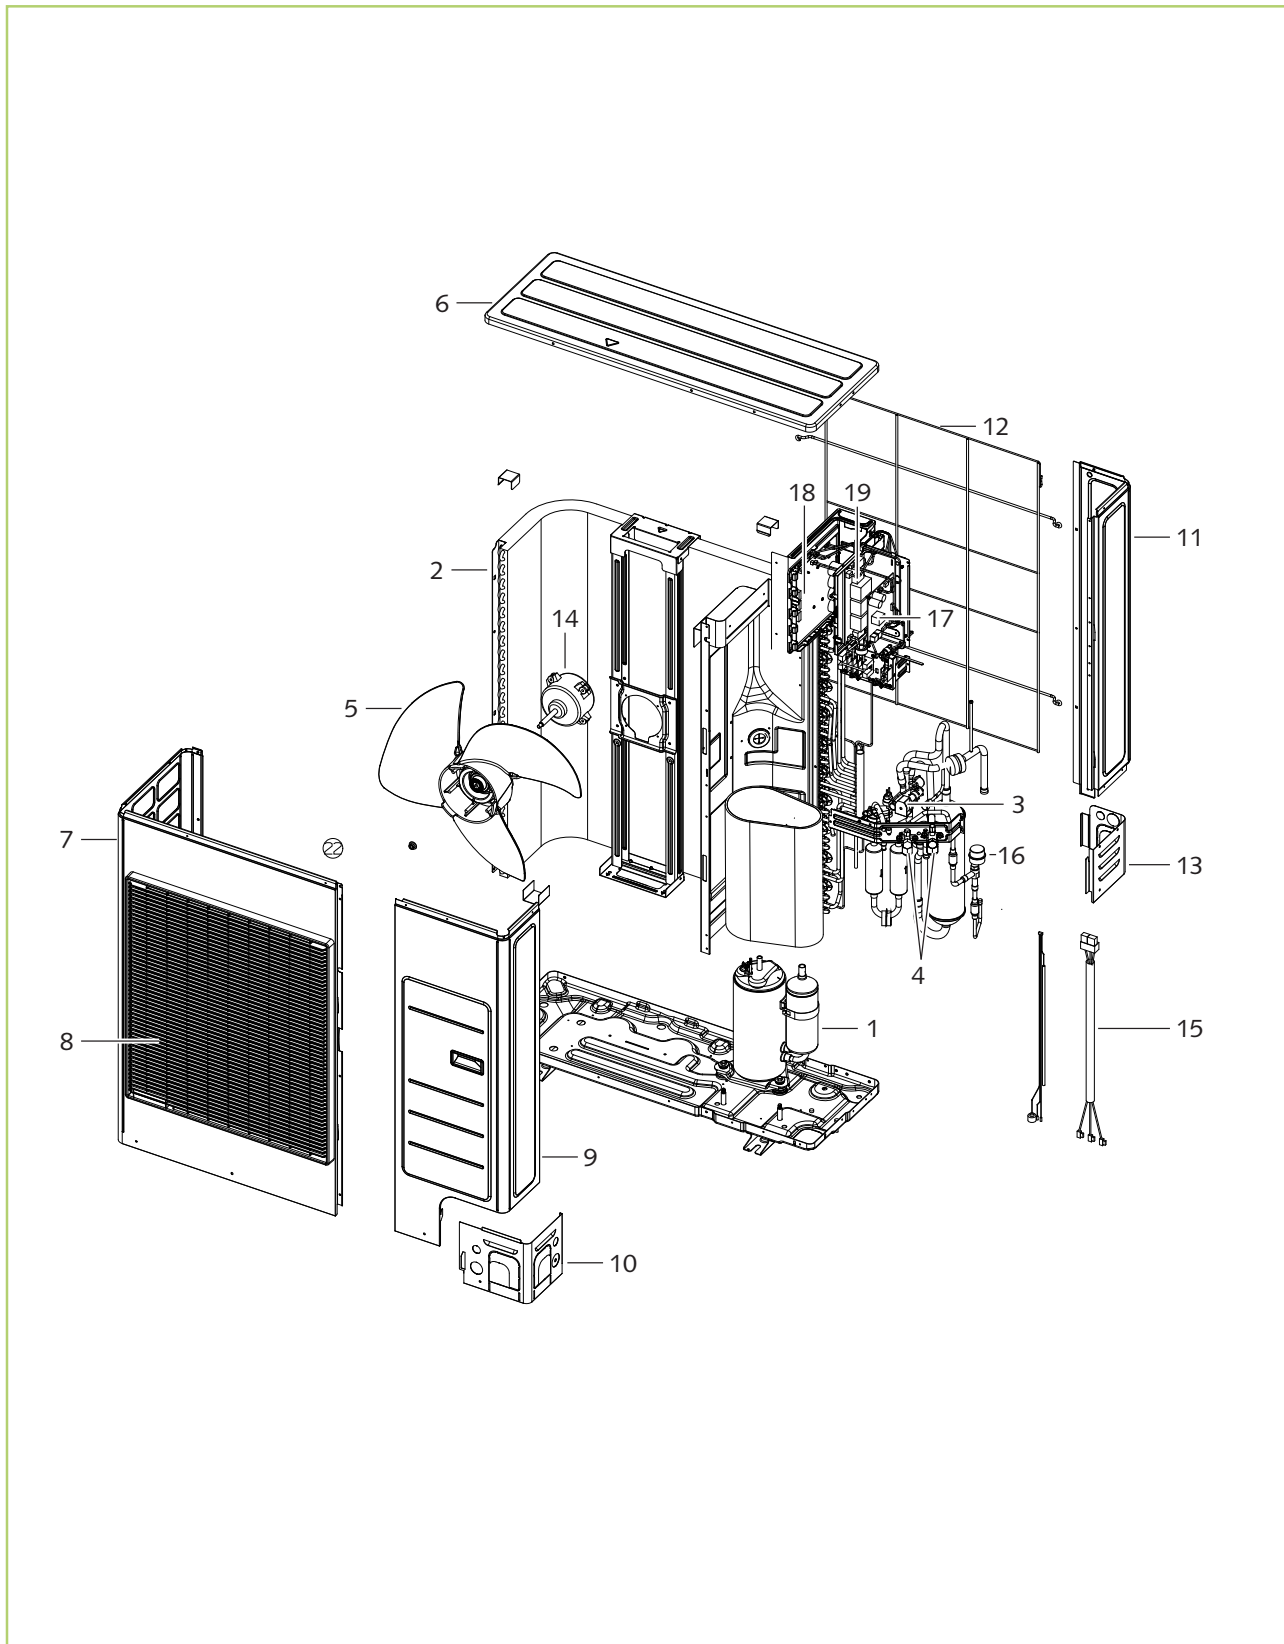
Explosionszeichnung Außenmodul WKF/WKF-compact 120
